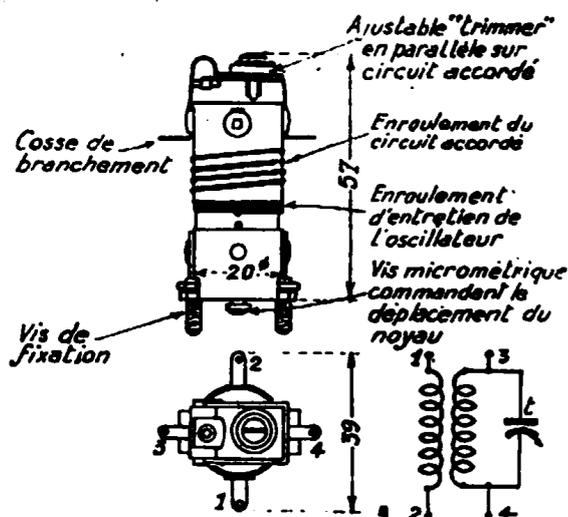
Exemple de self oscillatrice ondes courtes à noyau magnétique plongeur et portant son trimmer. 1° Enroulement d'entretien; 2° Enroulement d'entretien côté masse ou +HT; 3° Enroulement accordé côté grille; 4° Enroulement accordé côté masse ou padding.
